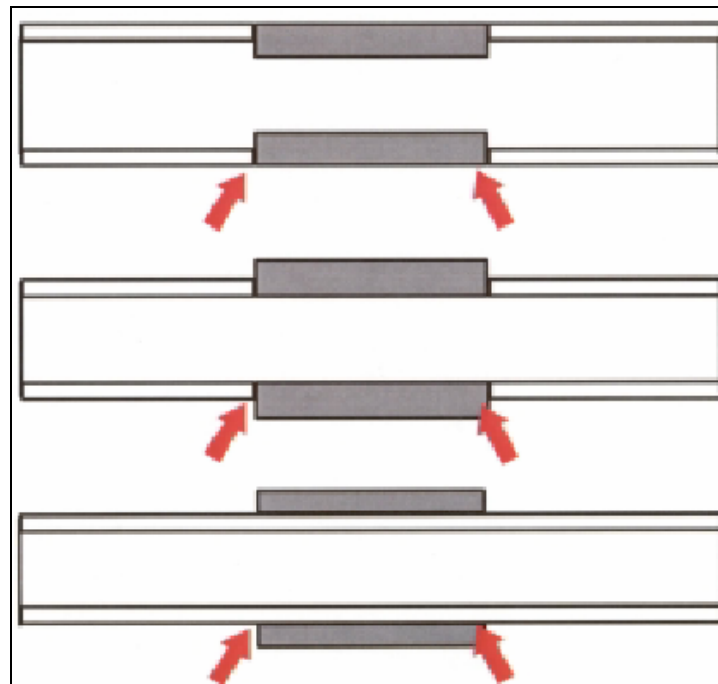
Tailor welded tubes: diâmetro exterior constante, diâmetro interior constante e “manga”¹.
